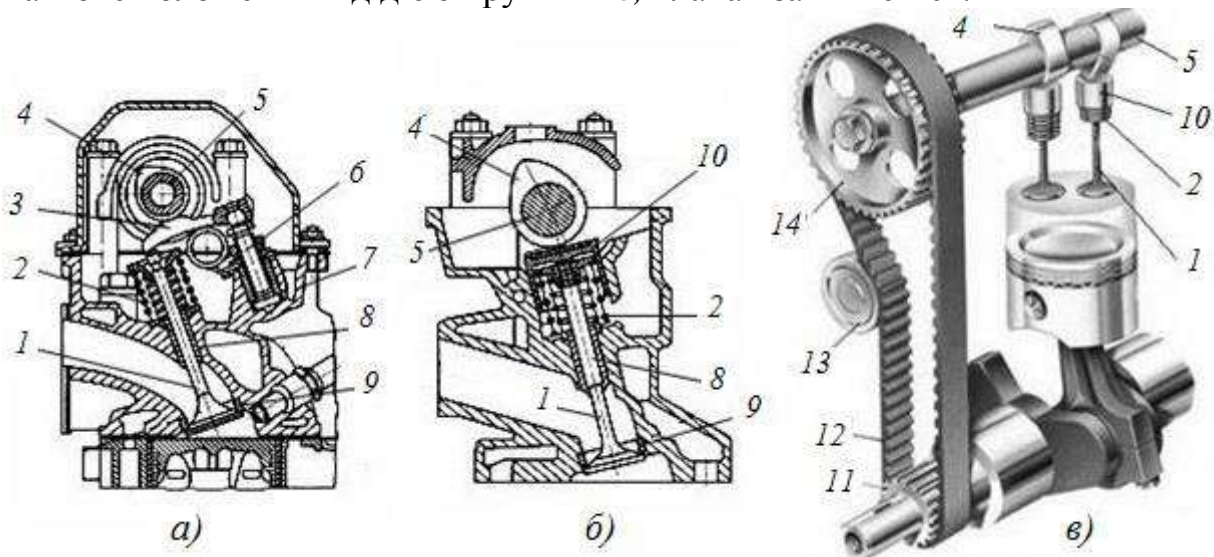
Механізми газорозподілу з верхнім розташуванням розподільного вала клапанів: з важелем (а), без коромисел (б), принципова схема з пасовим механізмом приводу (в):
